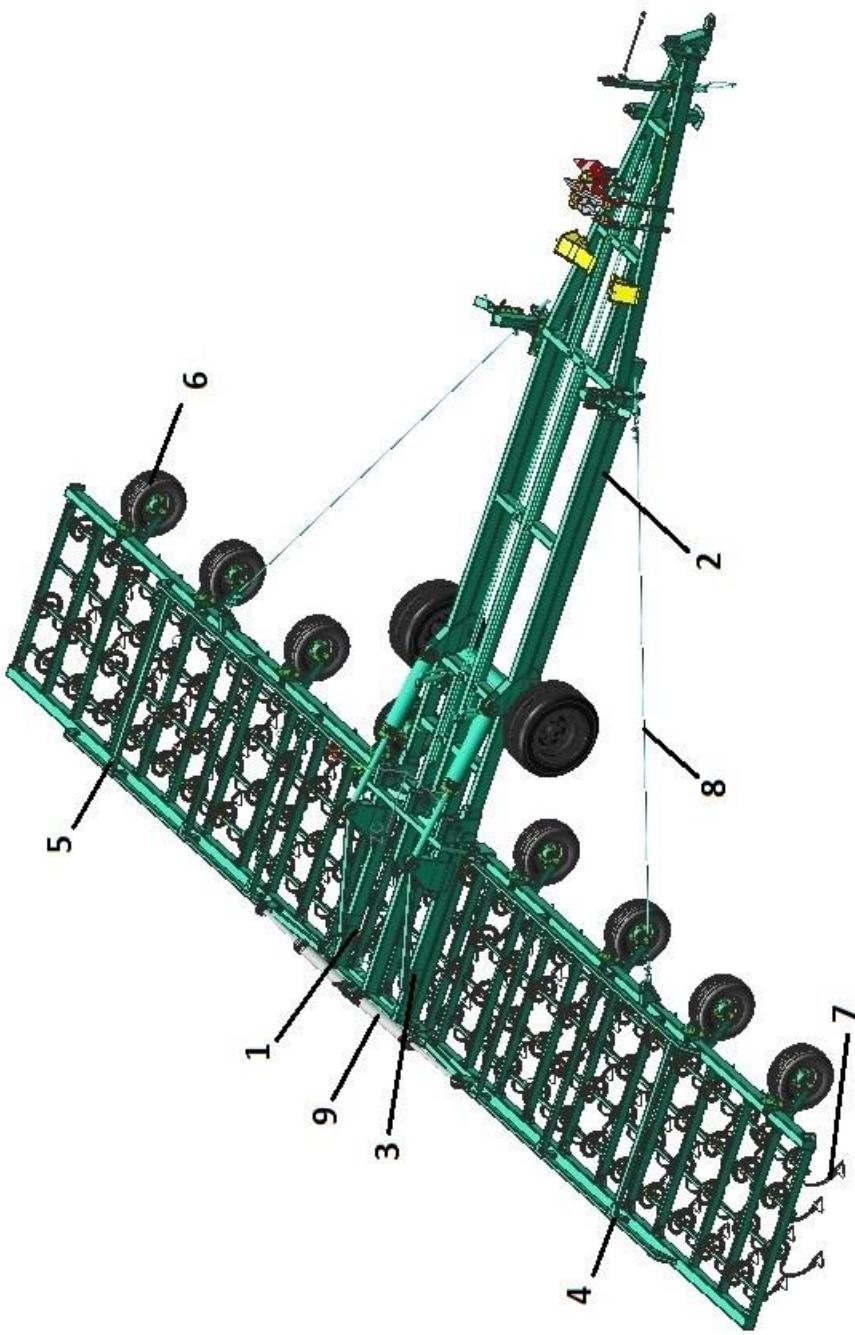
Общий вид культиватора КПМ-12ПЕ в рабочем положении
